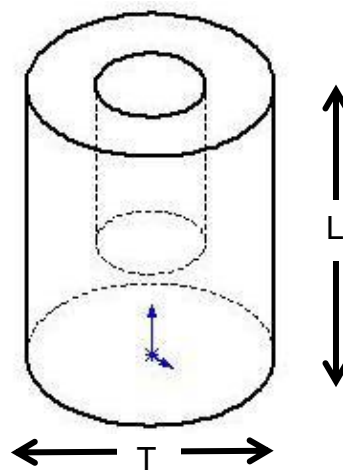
Geometría de las muestras (T) Sección transversal, (L) Sección Longitudinal
